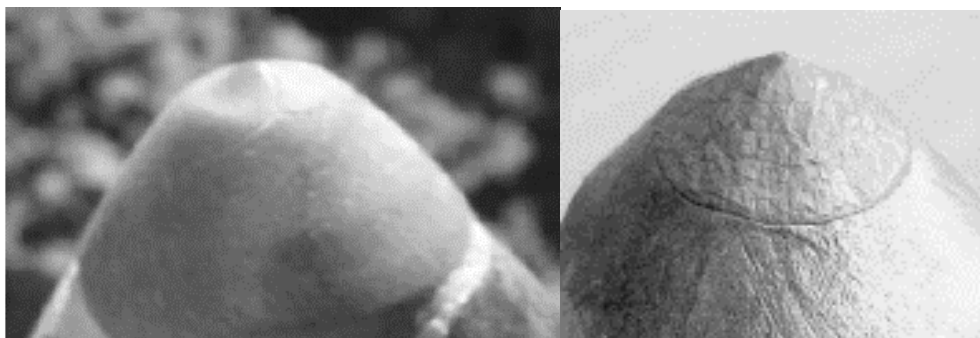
Вершина режущей вставки резца со следами выкрашивания
